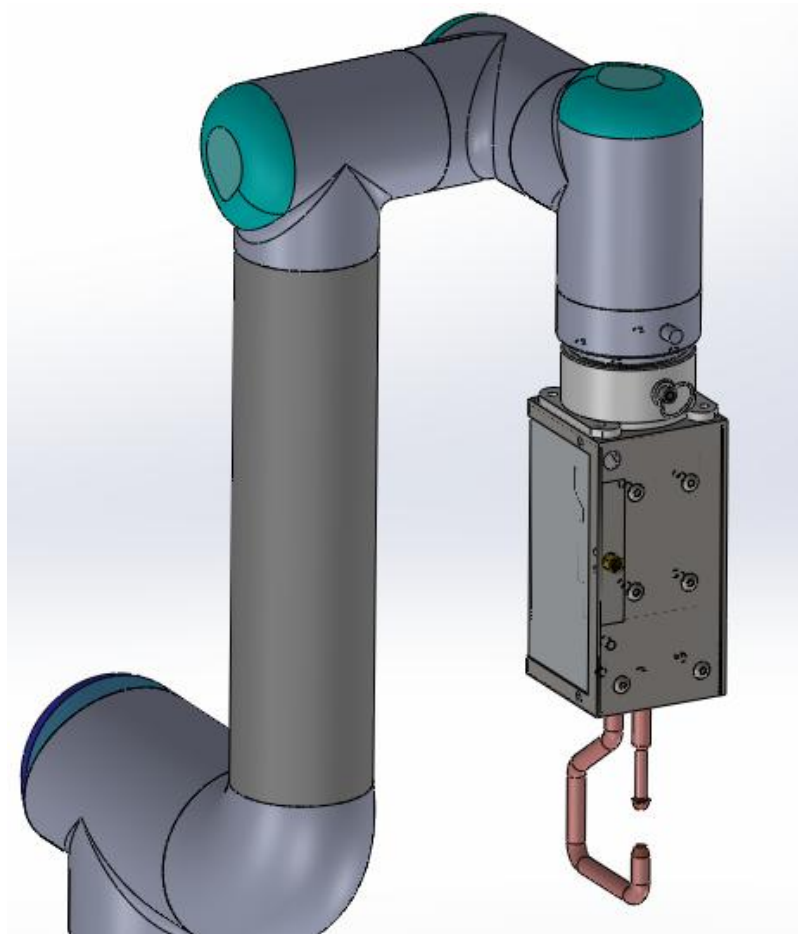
Vista isométrica pinza de soldadura por puntos
